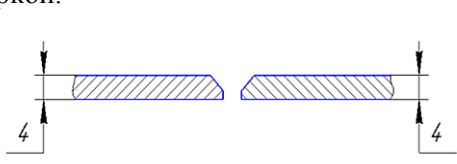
Конструкция сварного соединения с разделкой кромок.
